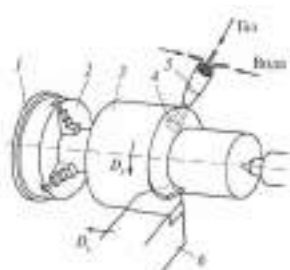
Схема процесу плазово-механічної обробки: 1 — струмоміпідвідне кільце; 2 — патрон; 3 — заготовка; 4 — плазова дуга; 5 — плазматрон; 6 — різальний інструмент
